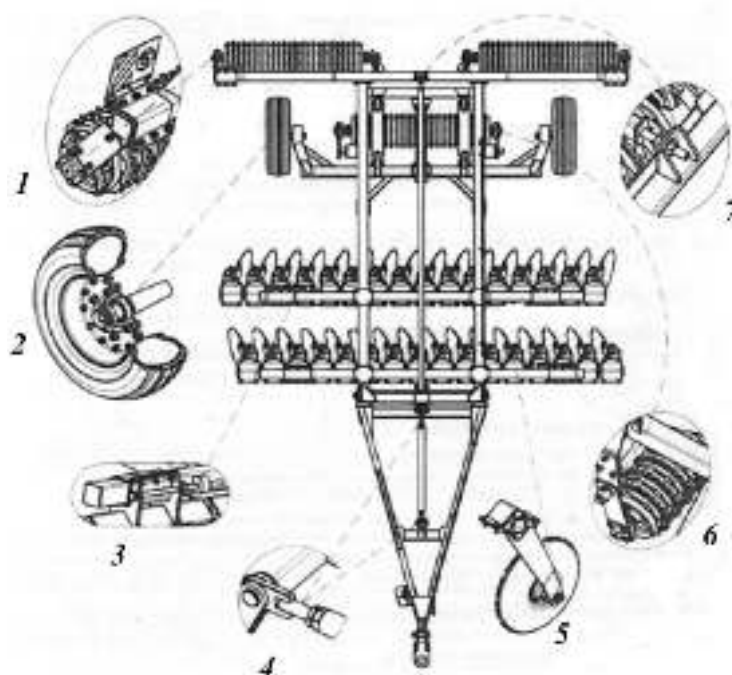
Схема смазки диска (к таблице 2.4)
